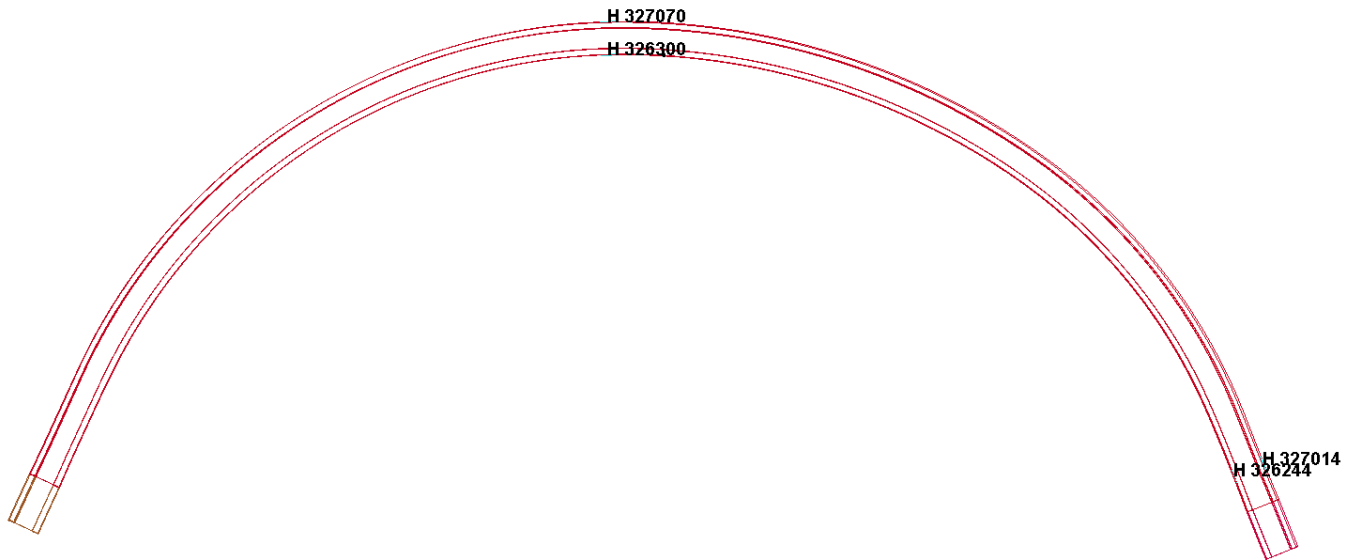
Контрольные элементы: середина заготовки (327070 – растянутая зона; 326300 – сжатая зона), свободный край заготовки (327014 – растянутая зона; 326244 – сжатая зона)
